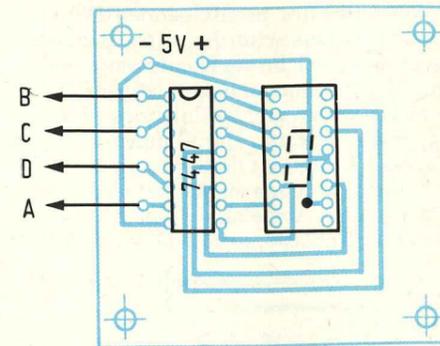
Bestückung der Anzeigeplatine. Die Anschlüsse A, B, C und D sind mit den gleich bezeichneten Punkten der Steuerplatine zu verbinden
